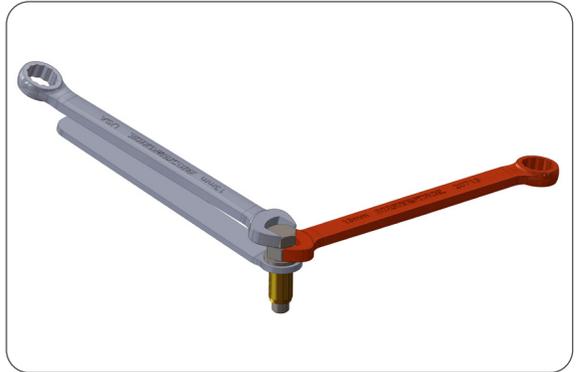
Blindnietmutter Setzung / threaded rivet setting
